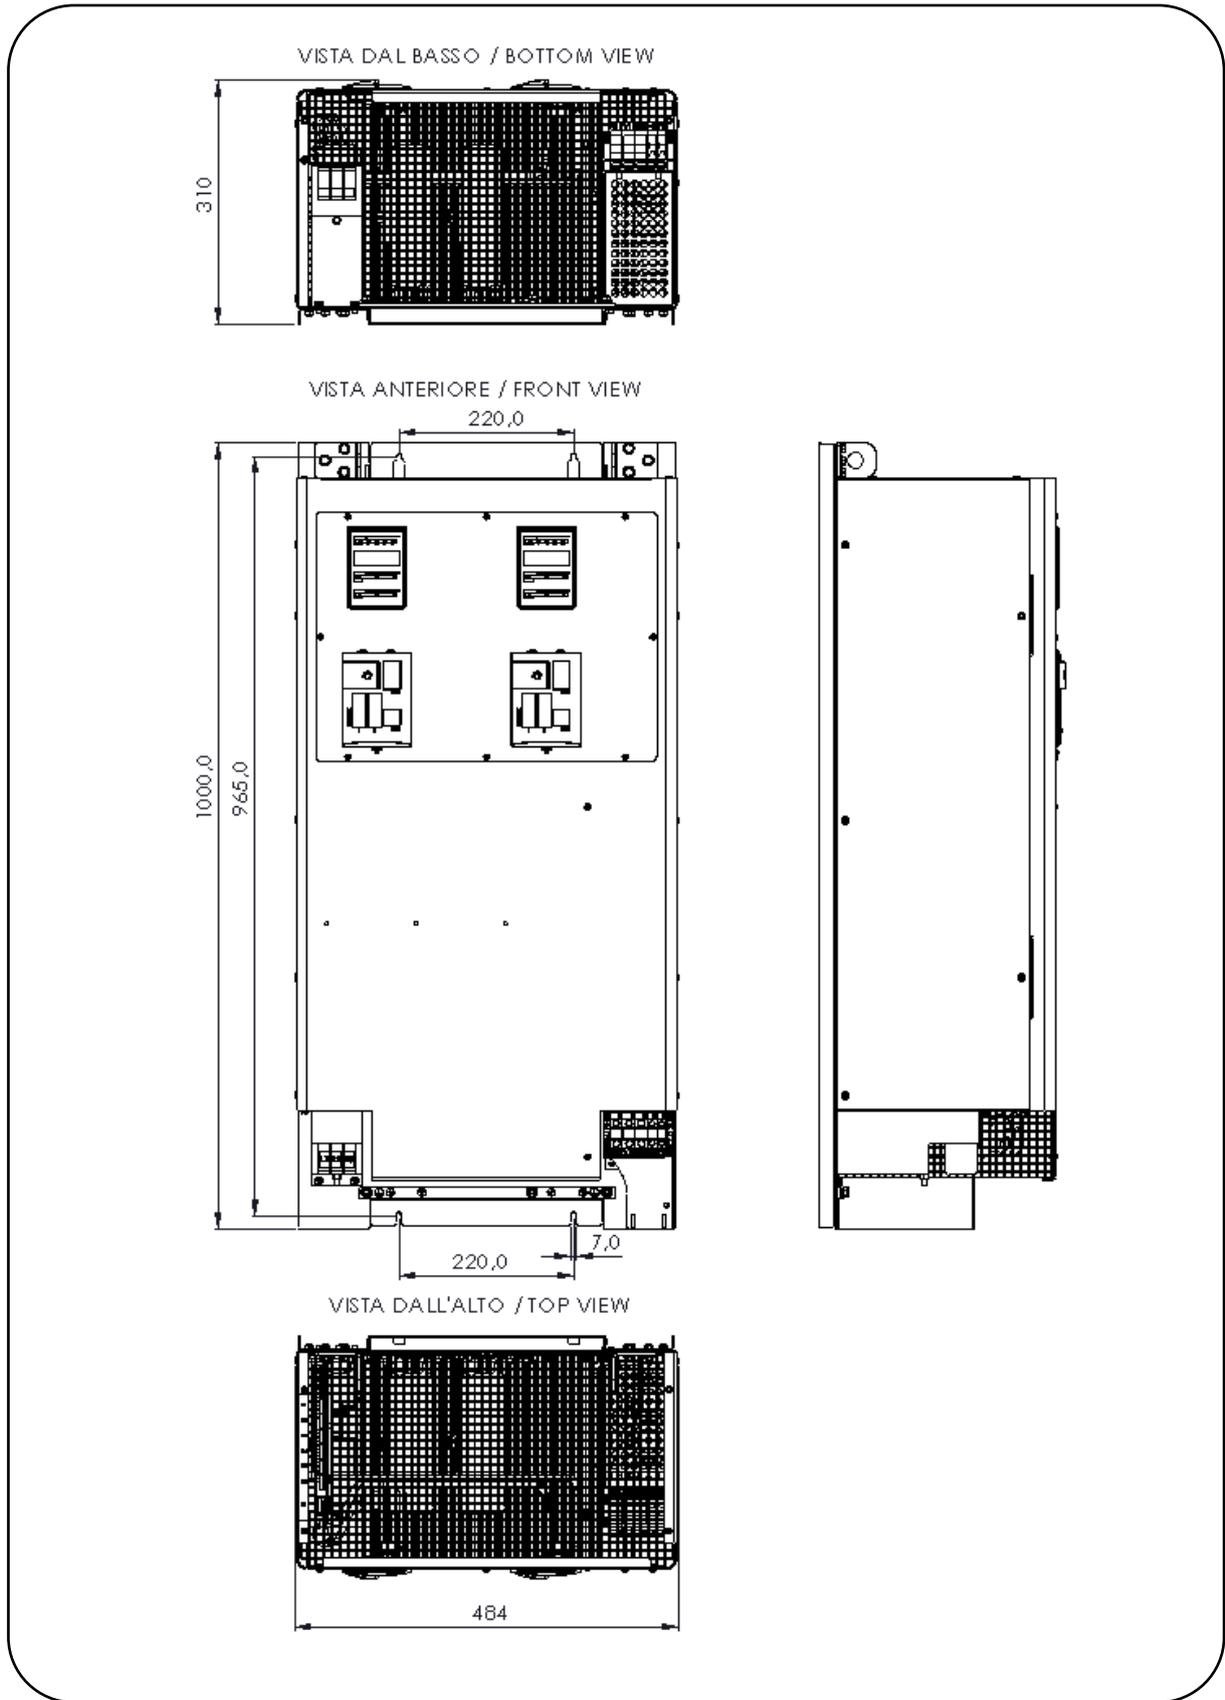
Dimensioni GE25, GE30 e GE40 / GE25, GE30 and GE40 dimensions
